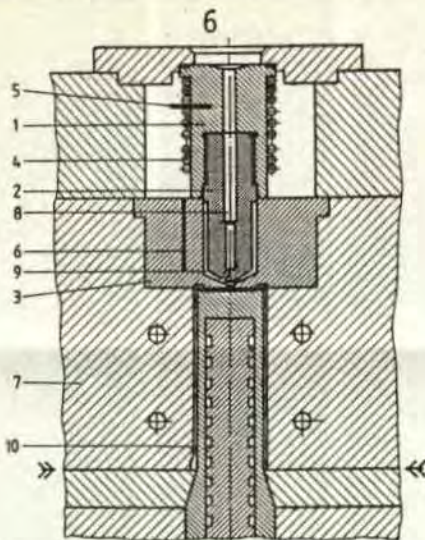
Detalle de un molde experimental con boquilla enchufada
